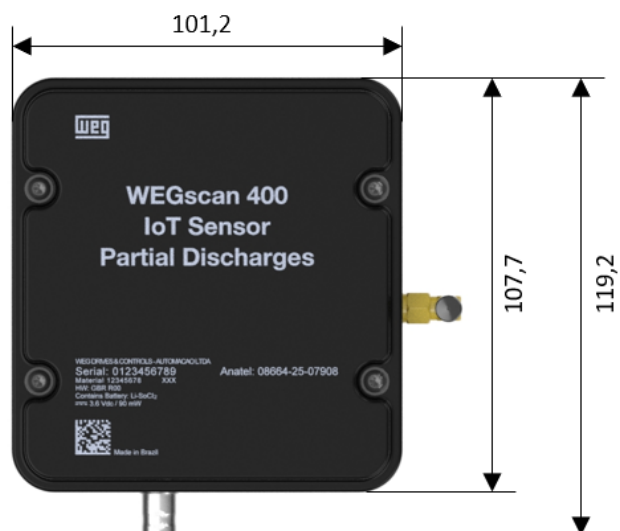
Dimensões [mm] externas do WEGscan400 com presilha para aletas - Vista superior
